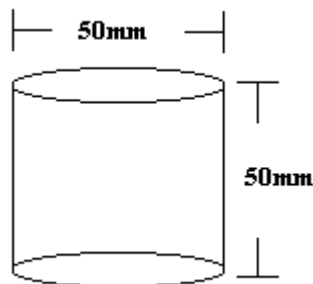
Dimensiones de probetas para ensayo de compresión.
